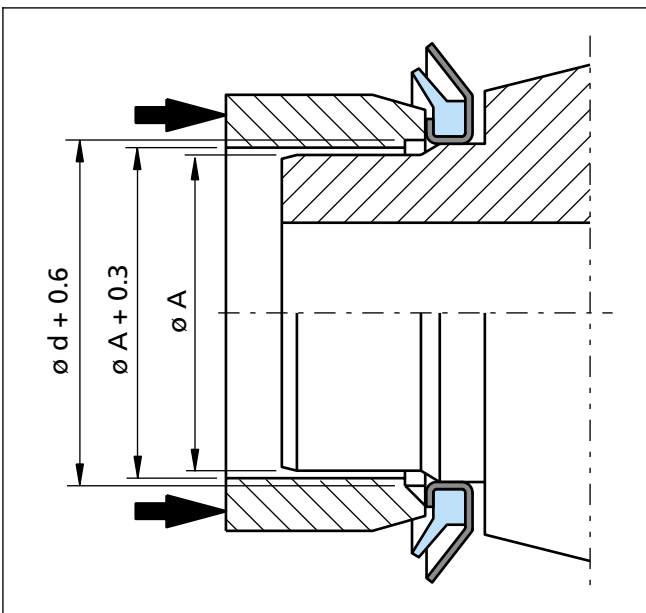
Montagewerkzeug. Bei der Montage gegen einen Ansatz darf die Montagekraft nicht zu groß sein, damit das Gehäuse des GAMMA-Ringes nicht beschädigt wird.
